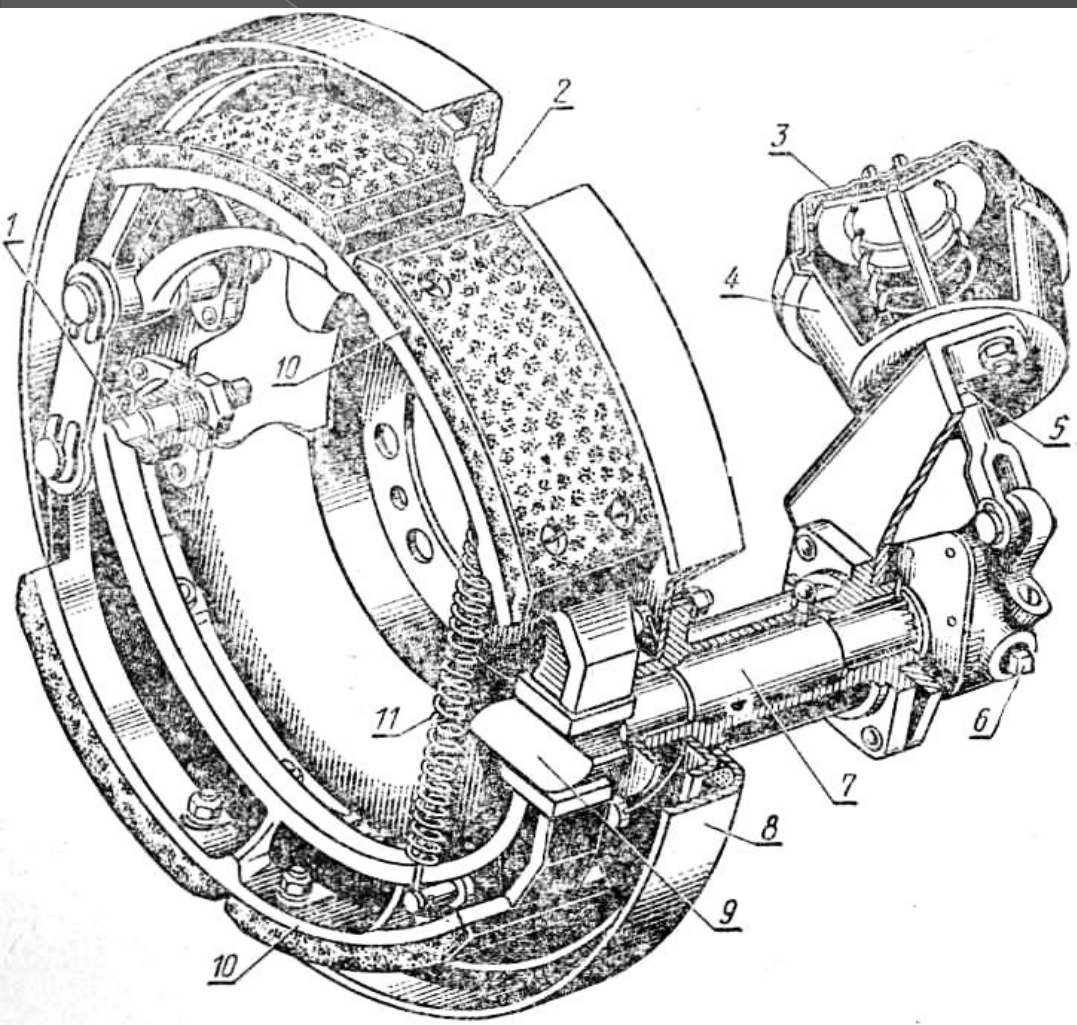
Колесный тормозной механизм колодочного типа с пневматическим приводом: 1 — опорные пальцы; 2 — неподвижный диск; 3 — диафрагма; 4 — корпус тормозной камеры; 5 — шток; 6 — головка оси червяка; 7 — вал разжимного кулака; 8 — барабан; 9 — разжимный кулак; 10 — колодки; 11 — втяжная пружина
